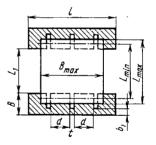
Конструкция контактных площадок для монтажа навесных конденсаторов
